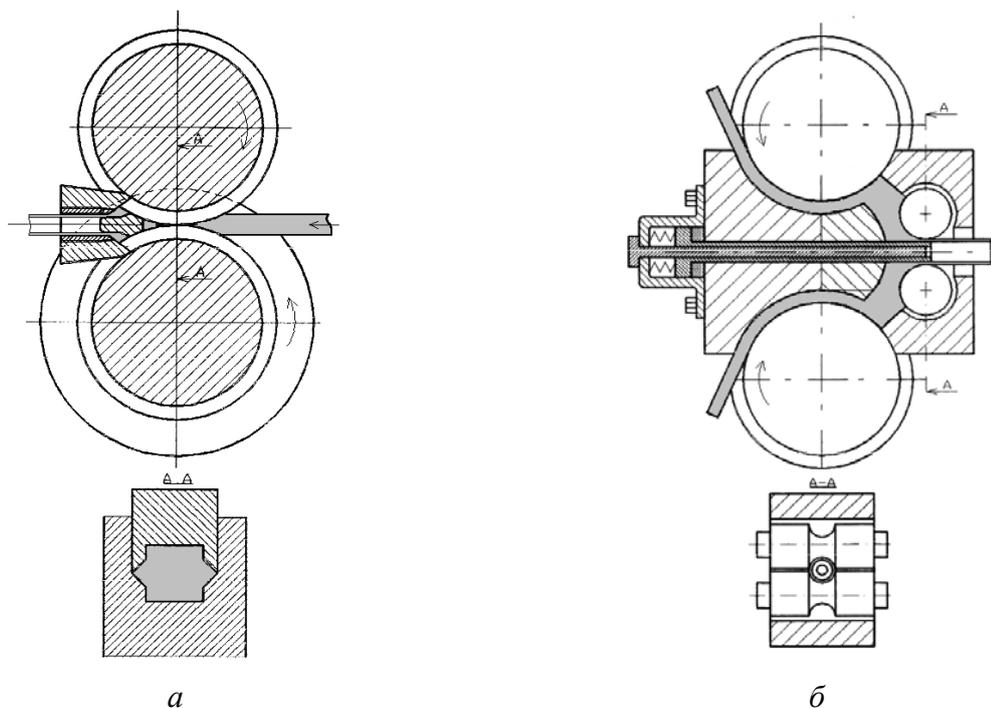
Устройства для получения сварных труб (а) и длинномерных полых изделий (б)
